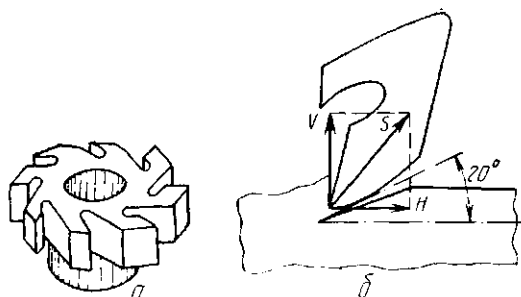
Общий вид фрезы для обработки уреза деталей низа обуви (а) и силы, действующие на материал при фрезеровании (б)
